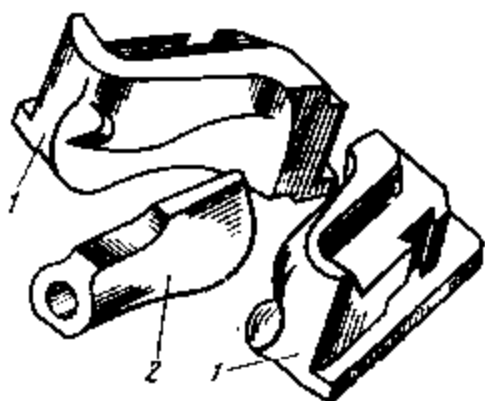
Рабочие инструменты машины для формования пяточной части заготовки сандалий
